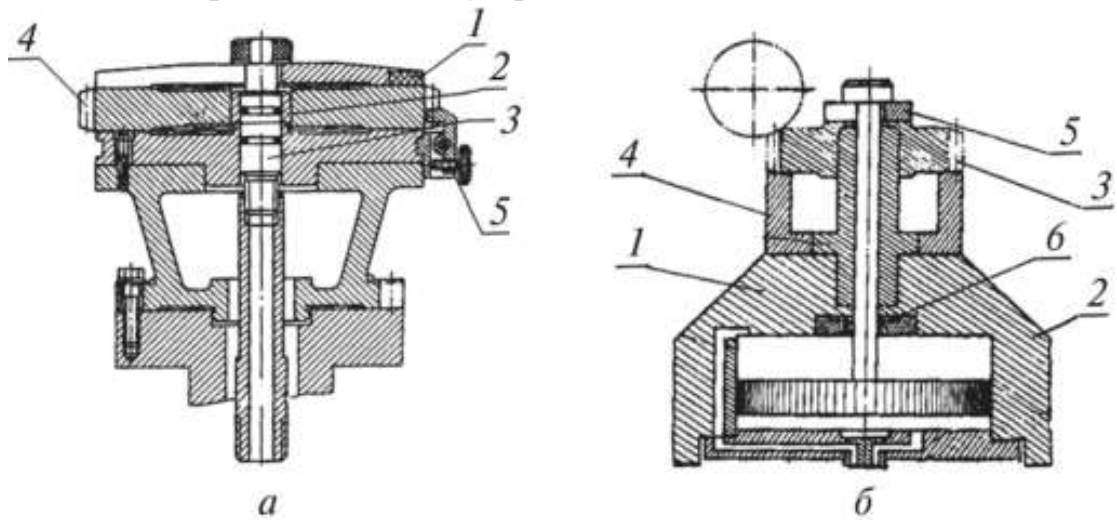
Схема ручного (а) та автоматизованого (б) пристрою з фіксаторами для встановлення заготовок на зубофасочному верстаті
